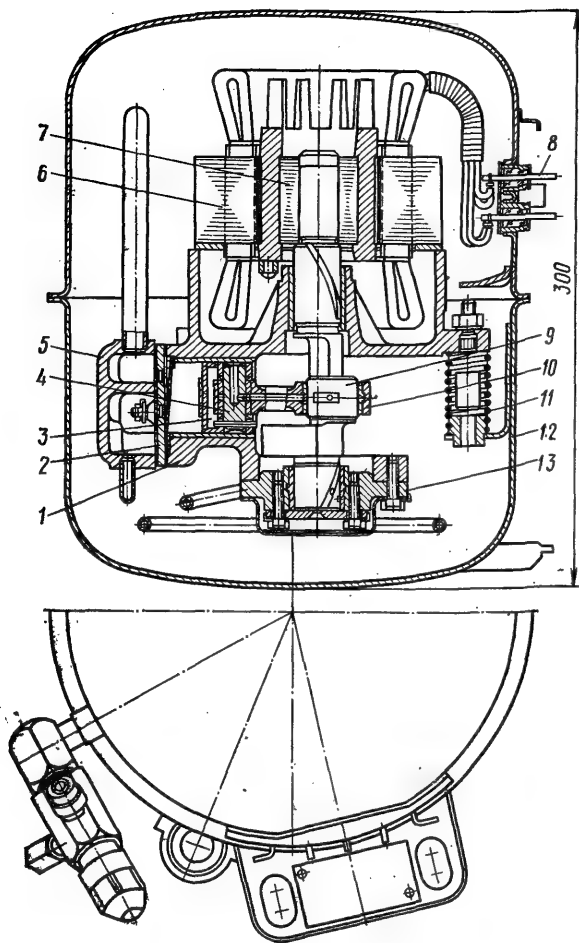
Герметичный высокооборотный компрессор ФГС 0,7~3 (2):
